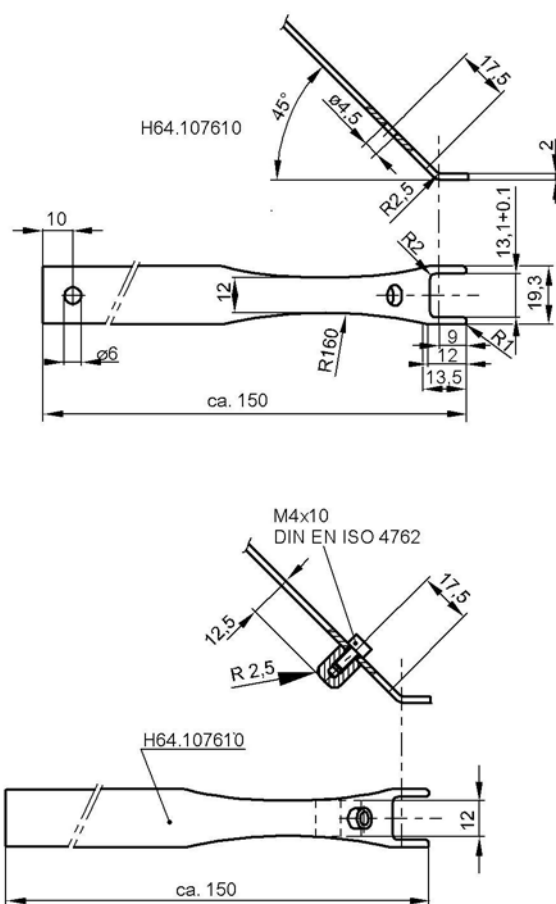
Werkzeug zum Lösen der Kabelstecker von den Magnetspulen
